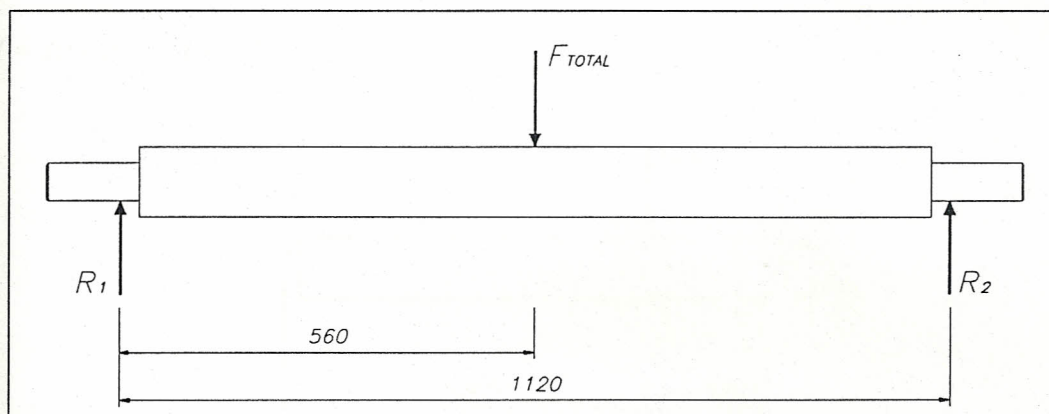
Esquema de dimensiones y fuerzas del eje embobinador.
